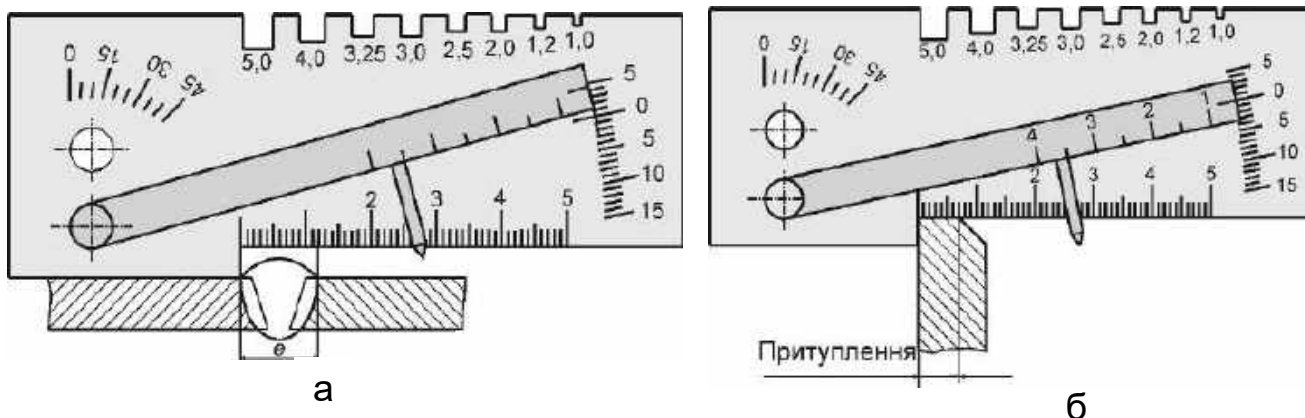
Схема вимірювання: а – ширини шва; б – притуплення крайки
